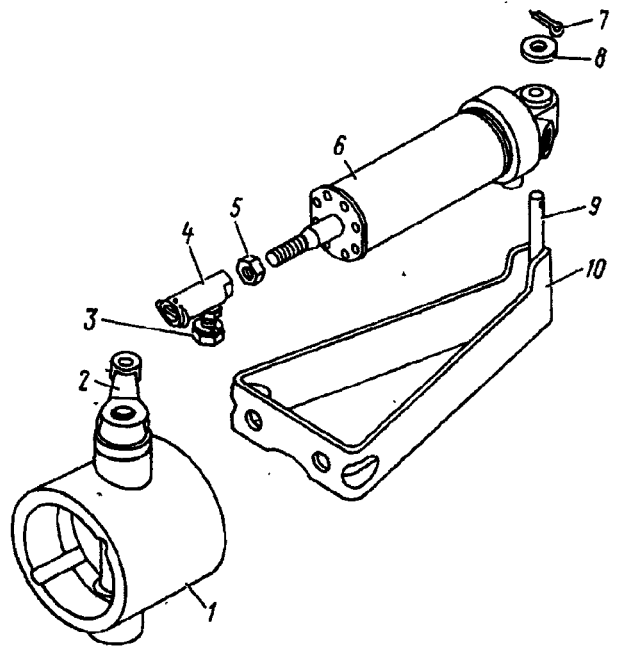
Установка пневматического цилиндра вспомогательной тормозной системы:
